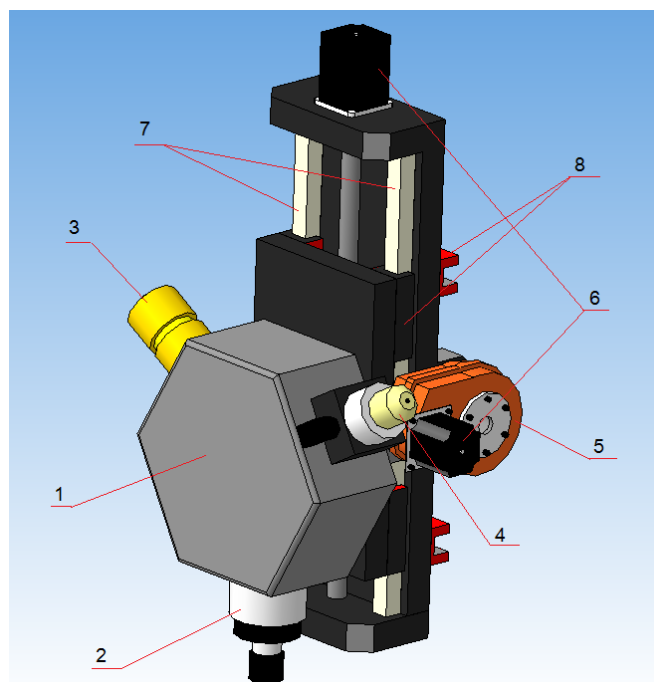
Проектная схема поворотной головки: 1 – поворотная головка; 2 – фрезерный шпindelь; 3 – плазматрон; 4 – лазерный резак; 5 – привод линейного перемещения; 6 – шаговые двигатели; 7 – рельсовые направляющие; 8 – каретки рельсовых направляющих
